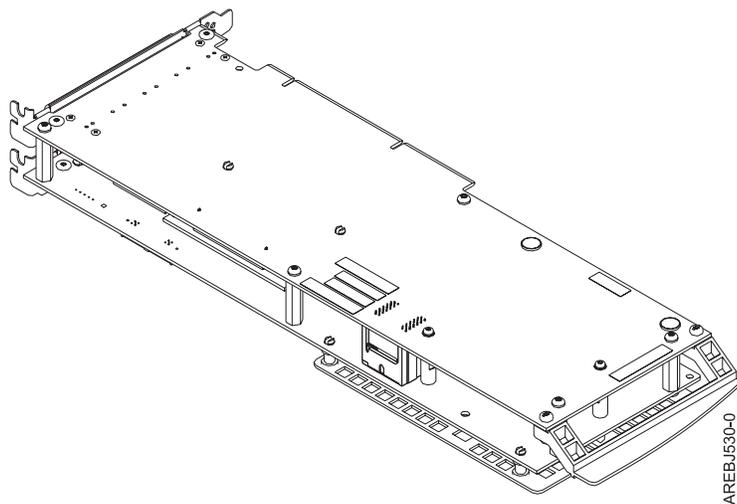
Adaptateur d'ensemble de cartes 572F/575C
